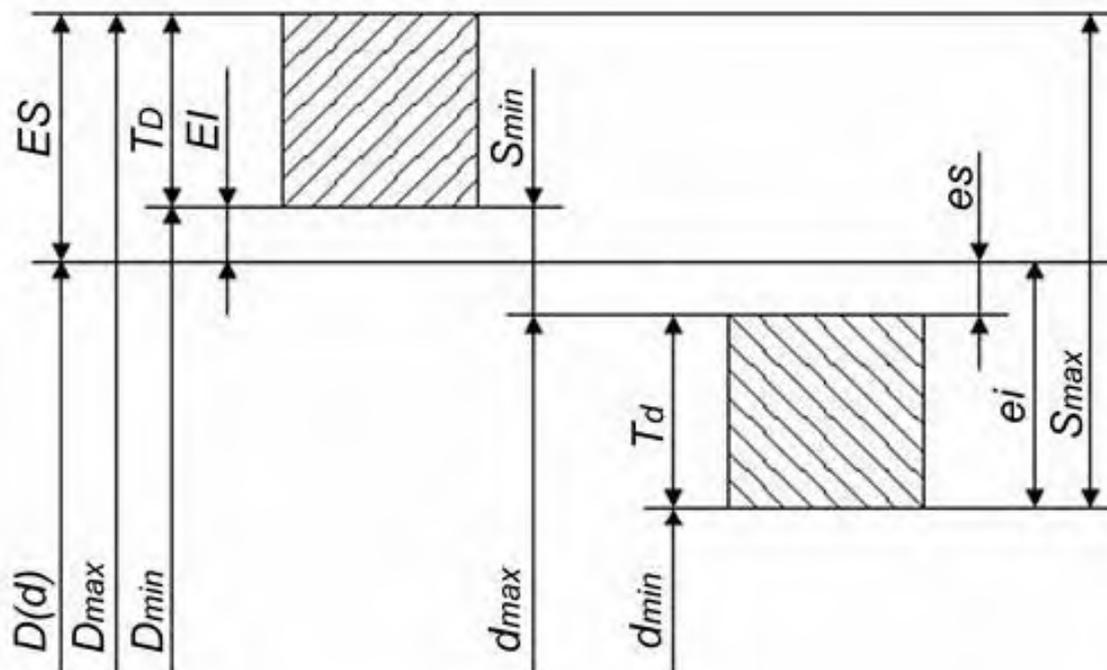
Поля допусков отверстия и вала при посадке с зазором
